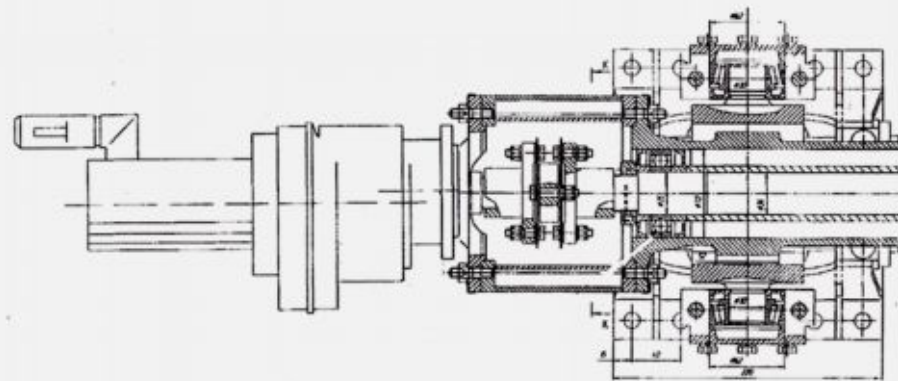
Установка мотор-редуктора на ходовом винте стержня
